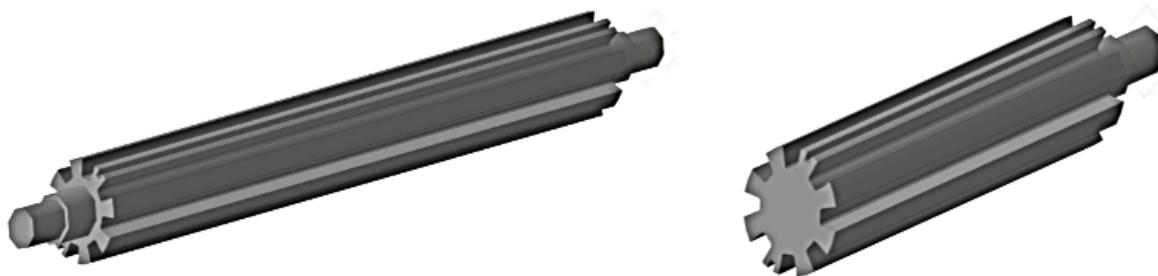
Внешний вид новой конструкции пильного цилиндра джина и его поперечного сечения
